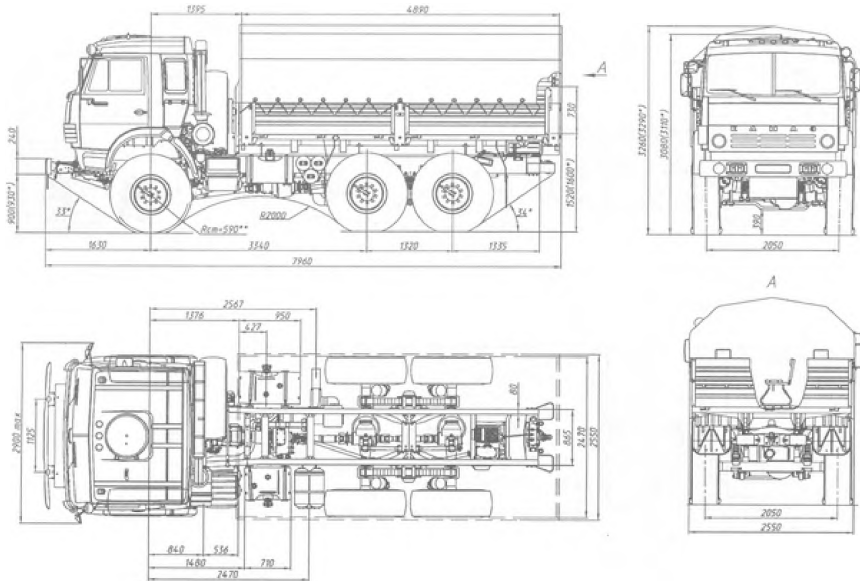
Автомобиль-тягач КАМАЗ-5350. Габаритные размеры.
